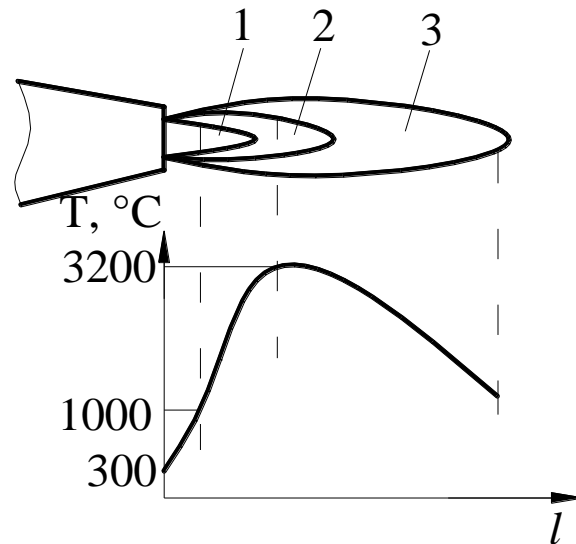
Строение газосварочного пламени: 1 — ядро пламени; 2 — средняя зона (сварочная); 3 — факел пламени
